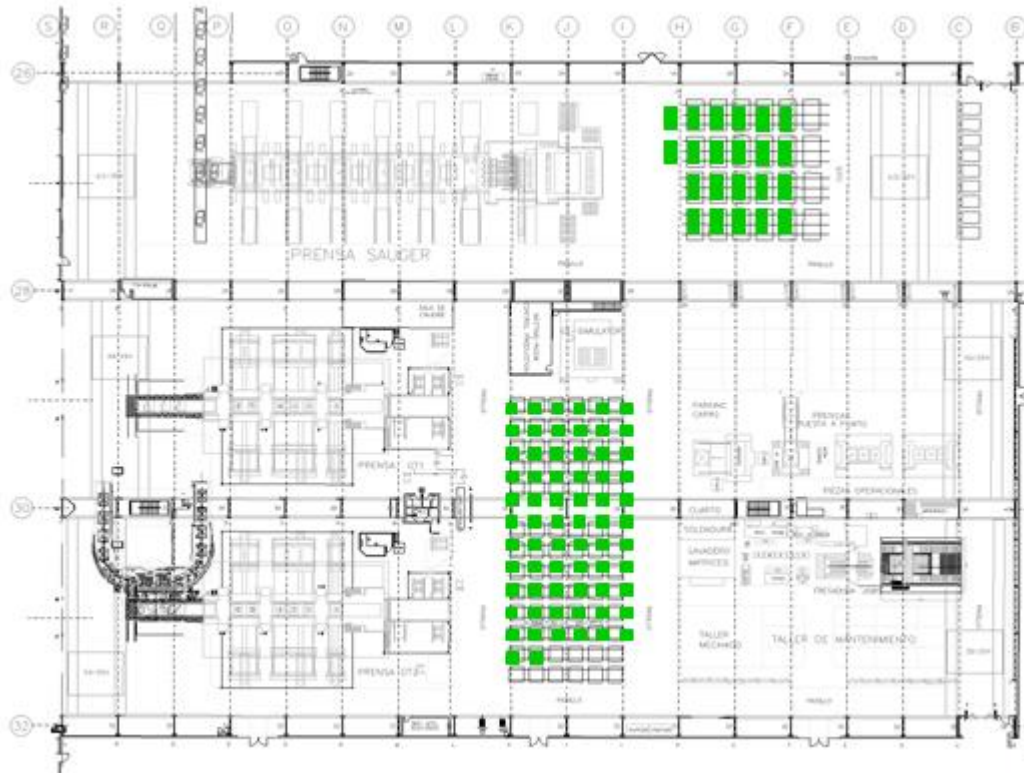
Plano con la ubicación de los troqueles en la nave de prensas de VW Navarra
